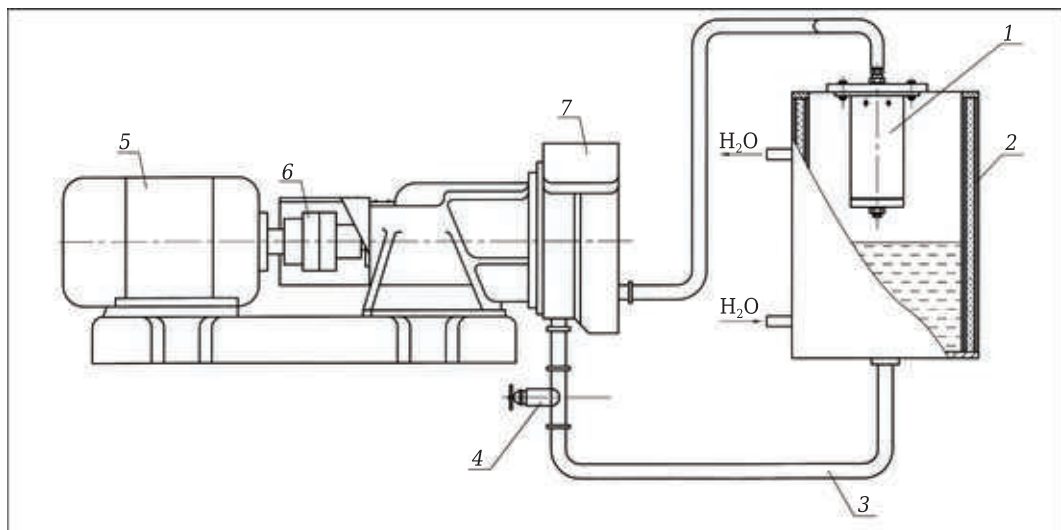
Схема проточного МДО при упрочнении втулок: 1 — приспособление для закрепления и оксидирования втулок; 2 — сборник электролита с рубашкой охлаждения; 3 — патрубок; 4 — кран; 5 — электродвигатель; 6 — муфта; 7 — щелочестойкий насос
